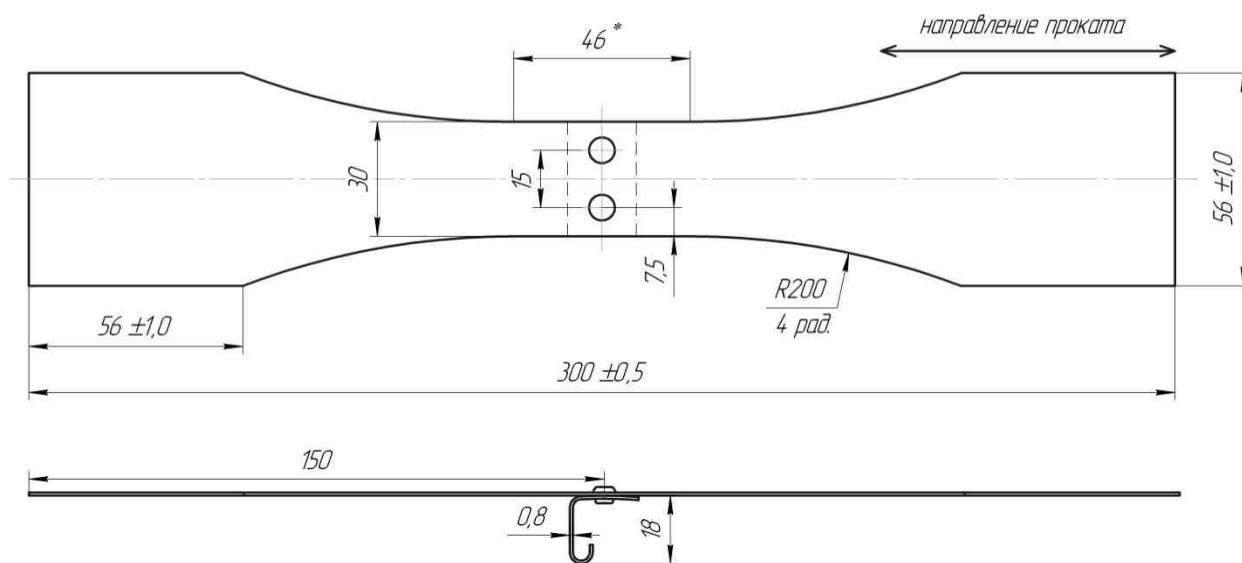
Фрагмент чертежа образцов с заклепками с плоско-скругленной закладной головкой
